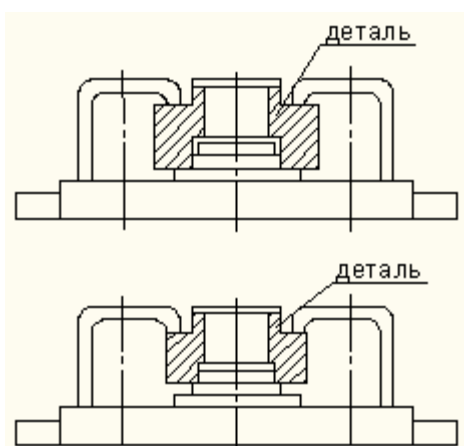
Схемы установки деталей на специальное приспособление для групповой обработки.
